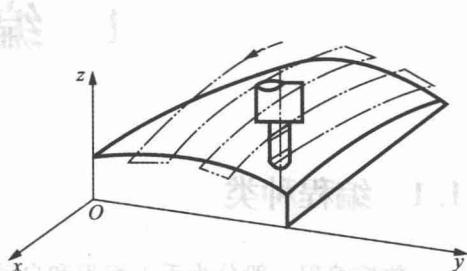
、5 坐标数控铣床加工零件变斜角面
